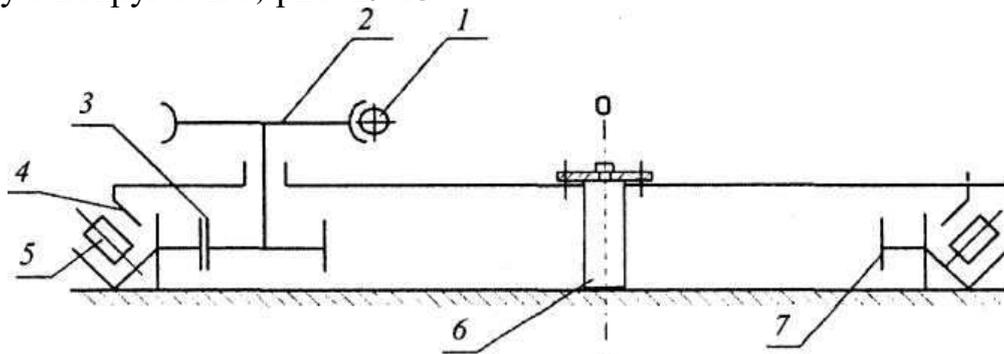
Схема механизма поворота: 1 - червяк; 2 - червячное колесо; 3 - шестерня привода поворота; 4 - плита; 5 - ролик; 6 — осевой коллектор; 7 — зубчатый венец
